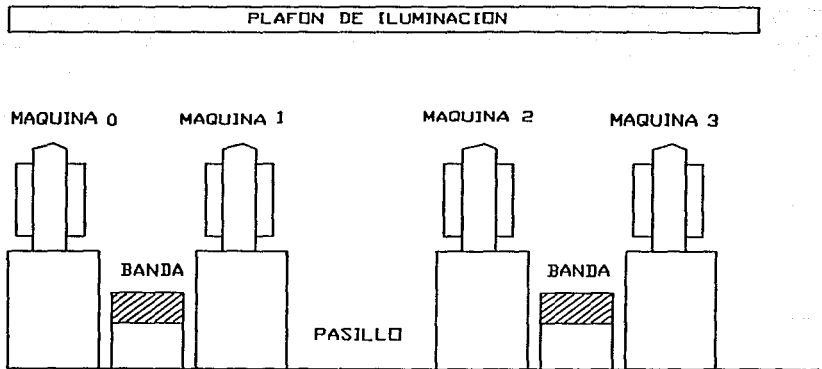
Vista frontal de las máquinas soldadoras
